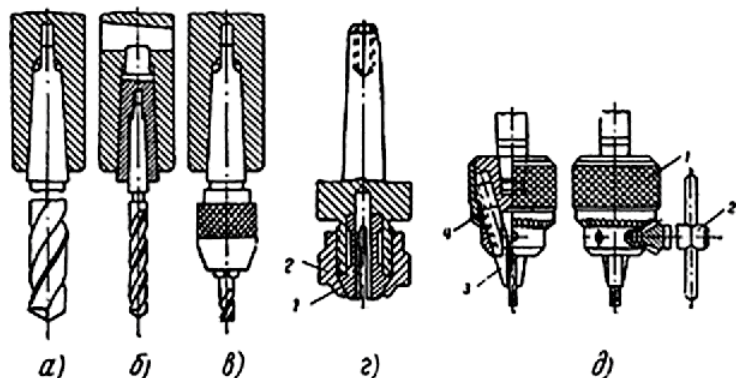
Приспособления для зажима инструмента при сверлении:
